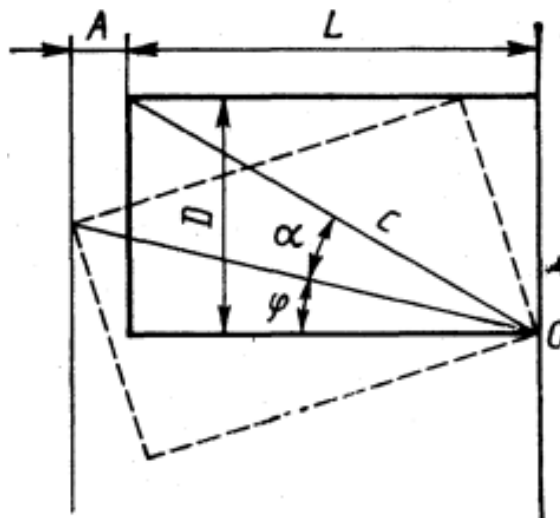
Розрахункова схема лотка-скату коробчастого типу [3]
